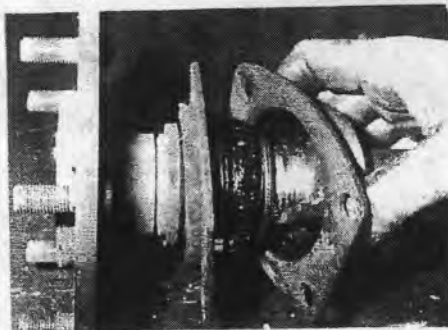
; Dan verschijnt het (dubbele) lager. De buitenste schaal van het achterste lager
